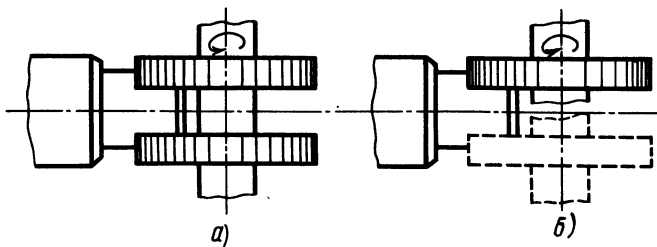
Обработка лысок двумя двусторонними дисковыми фрезами (а) и одной трехсторонней дисковой фрезой (б)
